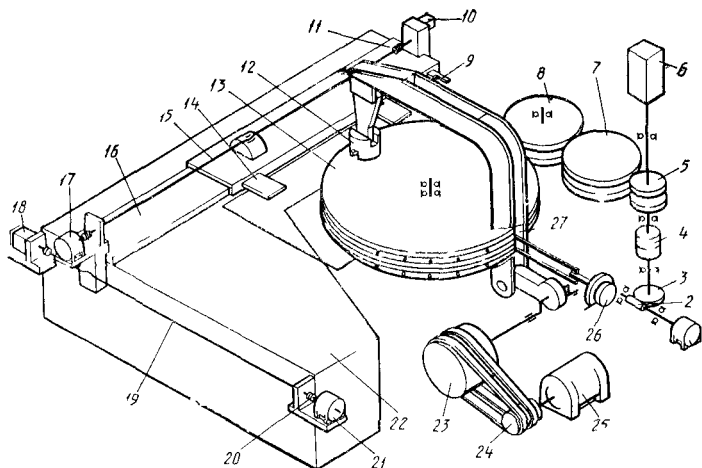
Кинематическая схема координатно-револьверного прес-са с ЧПУ
